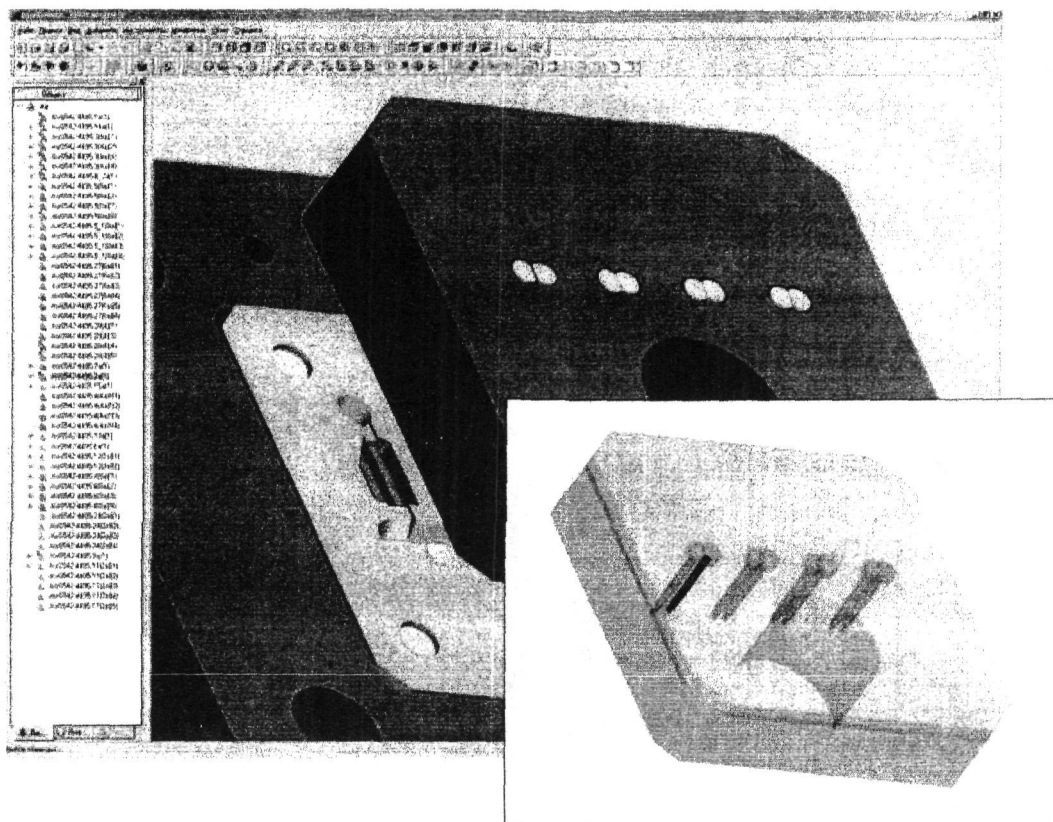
Проверка собираемости деталей «Обойма подвижная» и «Толкатель» в ADEM Assembly
